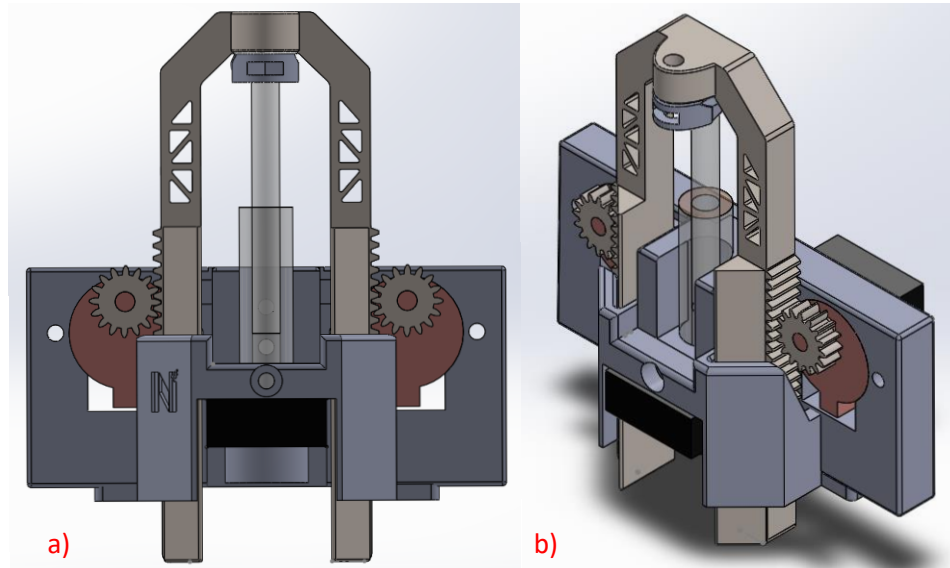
a) Vista frontal del prototipo; b) Vista isométrica del prototipo.
